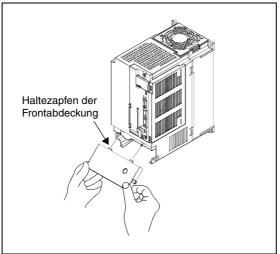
Schritt ①: Anbringen der Frontabdeckung
